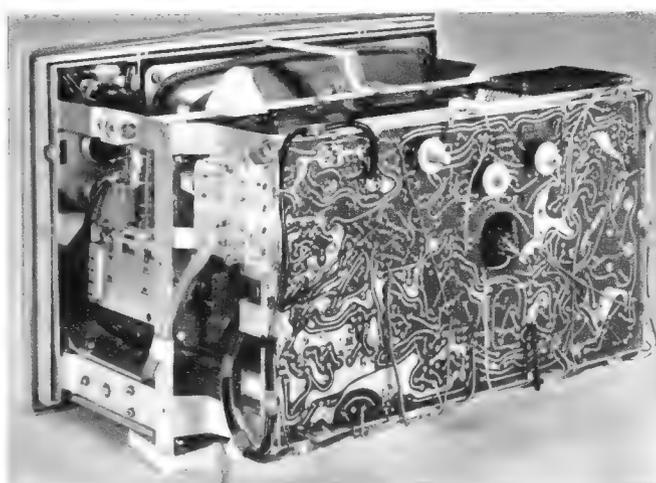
Der Chassisrahmen ist mit der Frontplatte verschraubt
